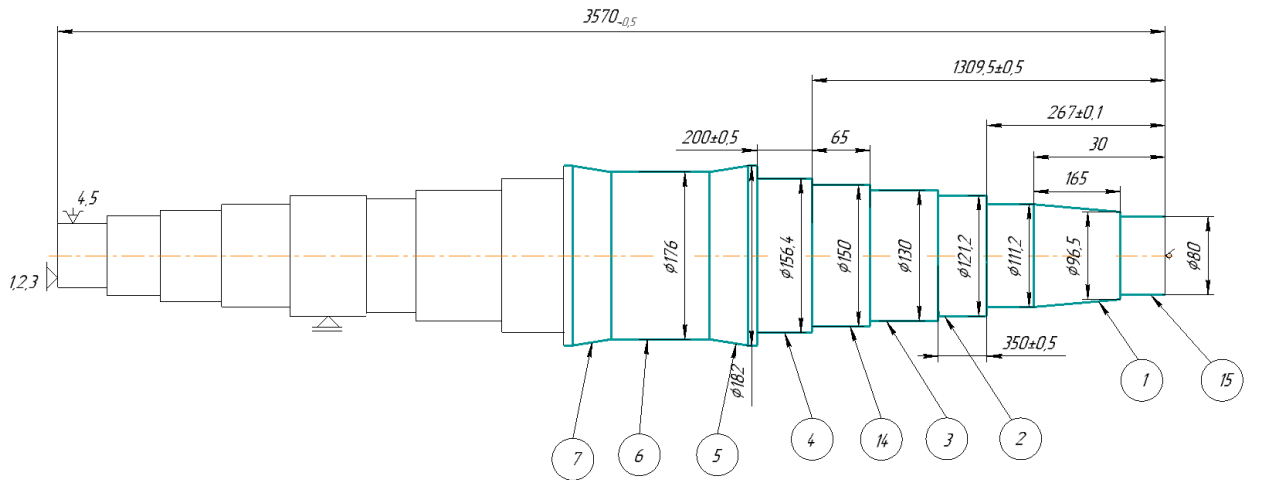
Базування деталі в трьохкулачковому патроні з рухомих центром
